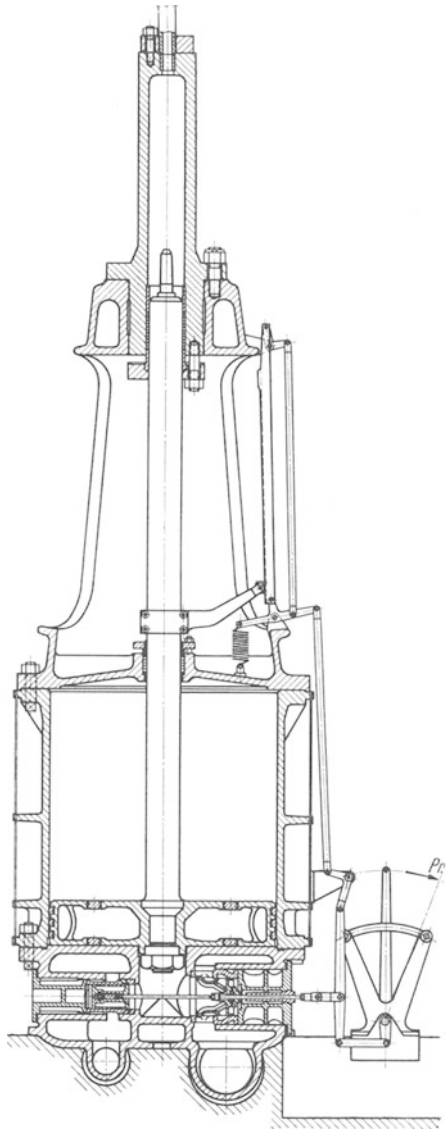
Dampftreibapparat mit oberem Druckwasserzylinder. Einbau der Steuerung im Zylinderboden. Antrieb des Abstellgestänges durch ein Lineal mit ablaufender Rolle. (Kreuser G. m. b. H., Hamm i. W.)
